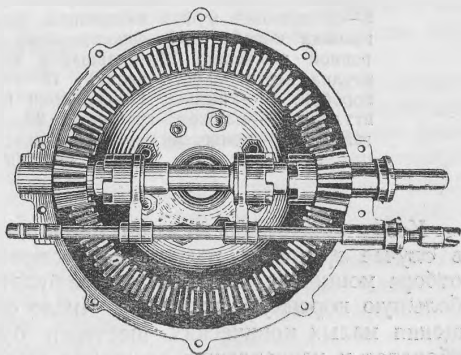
Верхняя половина картера реверсивной передачи с коронной шестерней, шлицевым валиком и валиком переключения с вилками (вид снизу).
